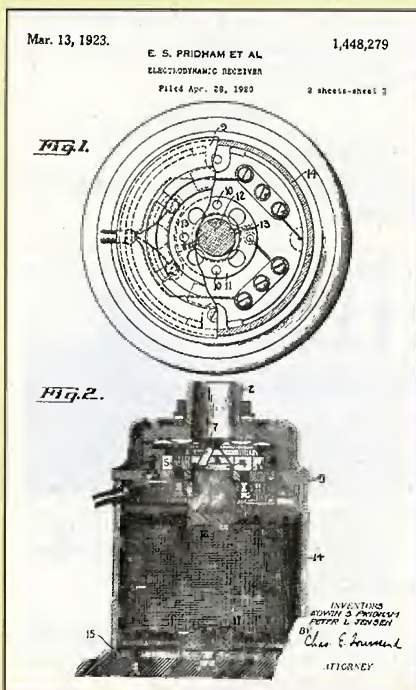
Detail spodní elektromagnetické části reproduktoru se zvukovým transformátorem
